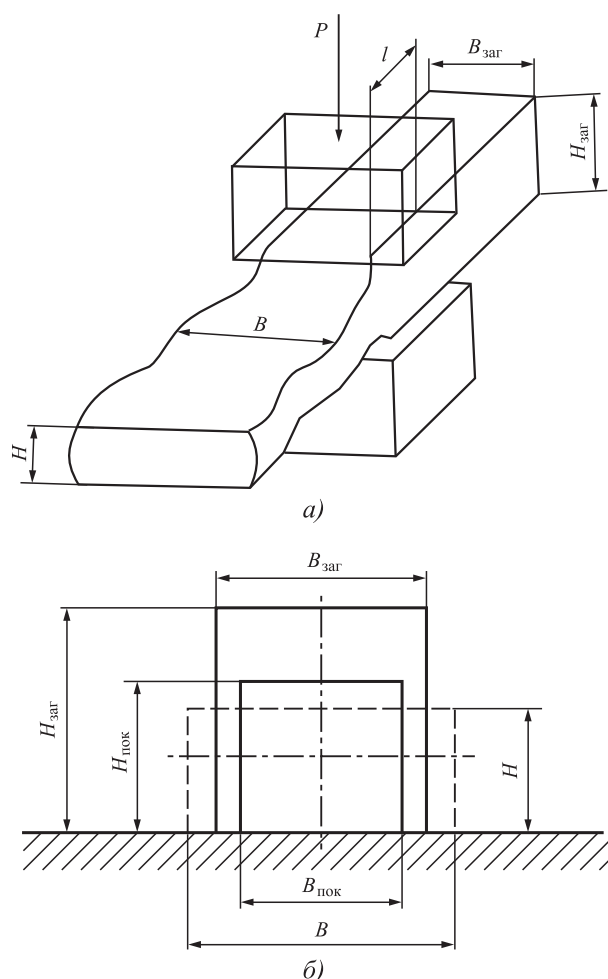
Схема процесса протяжки (а), исходная заготовка и поковка (б):
